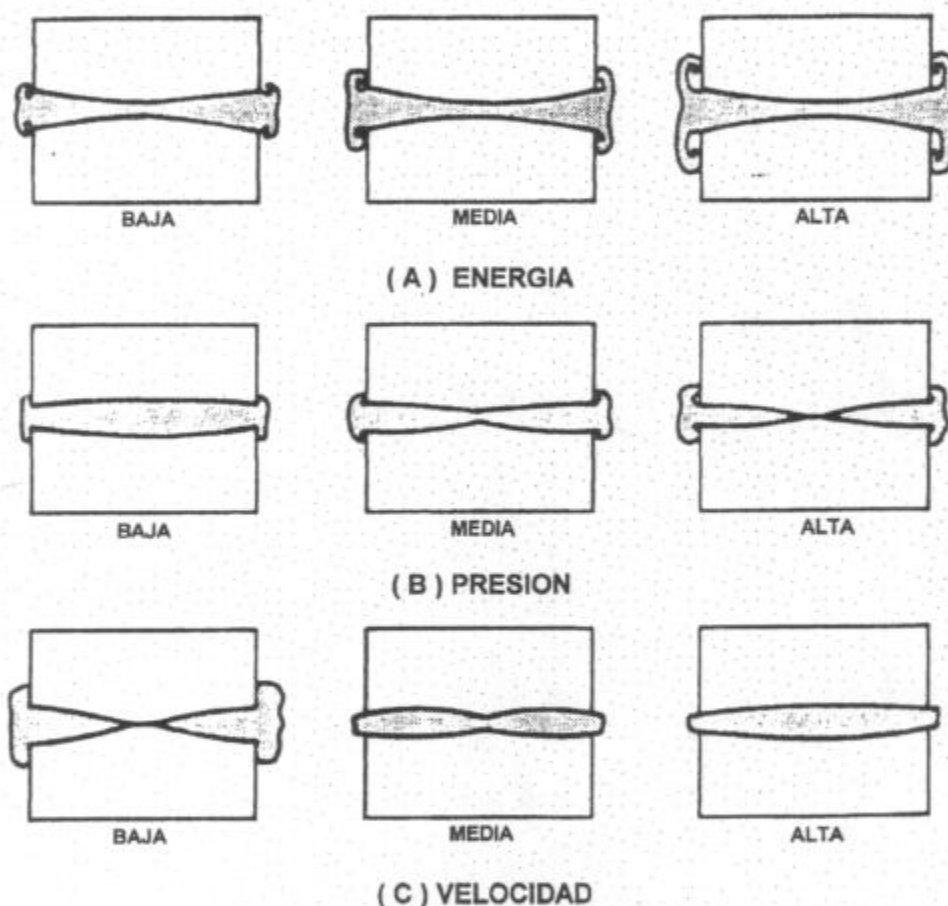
Efecto de las variables de soldadura (energía, presión y velocidad) sobre la interface de la junta en la formación de soldaduras por inercia.
